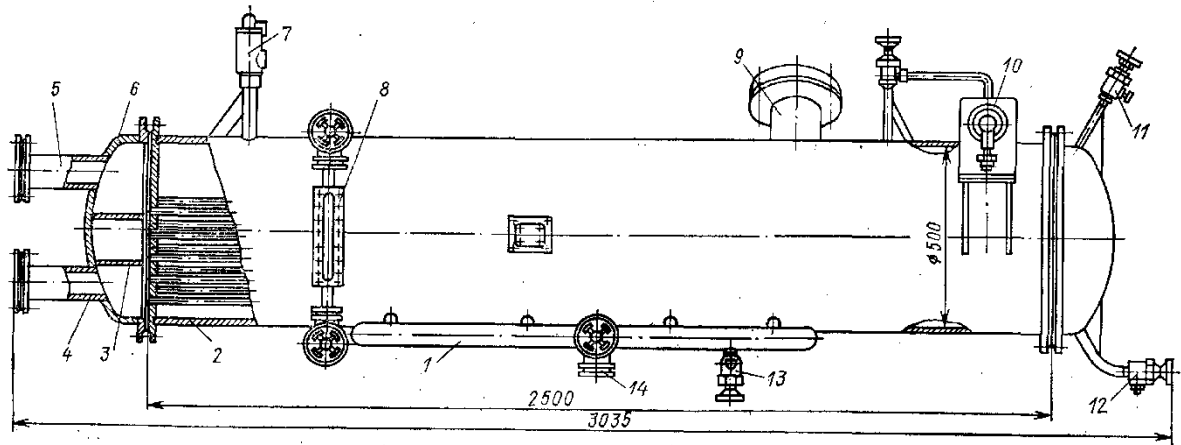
Фреоновий кожухотрубчастий випарник
